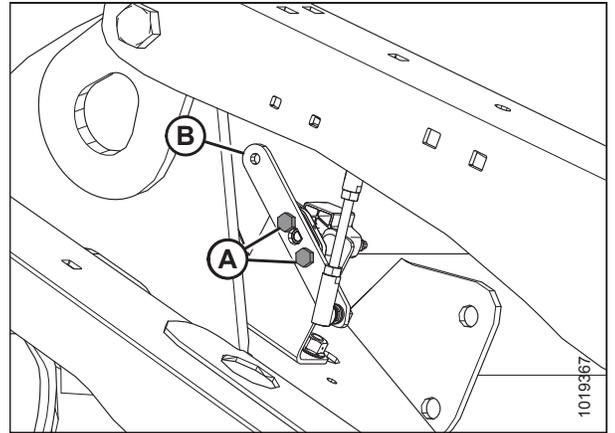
Haspelhöhsensor – Rechter Haspelarm
